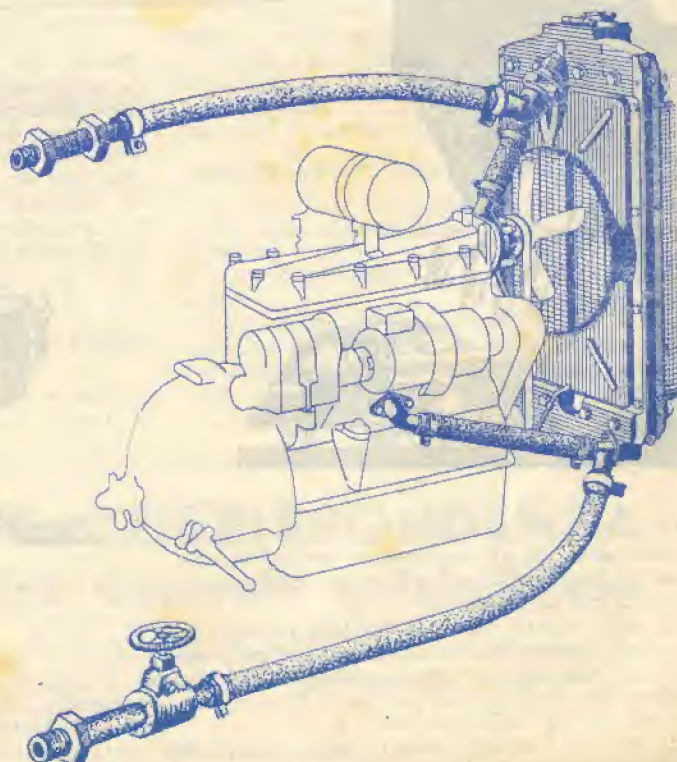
Di qui si deduce facilmente il metodo da adottare per il collegamento dei due tubi destinati al trasporto dell'acqua calda dal radiatore della macchina a quello di riscaldamento installato nell'interno della vettura.
